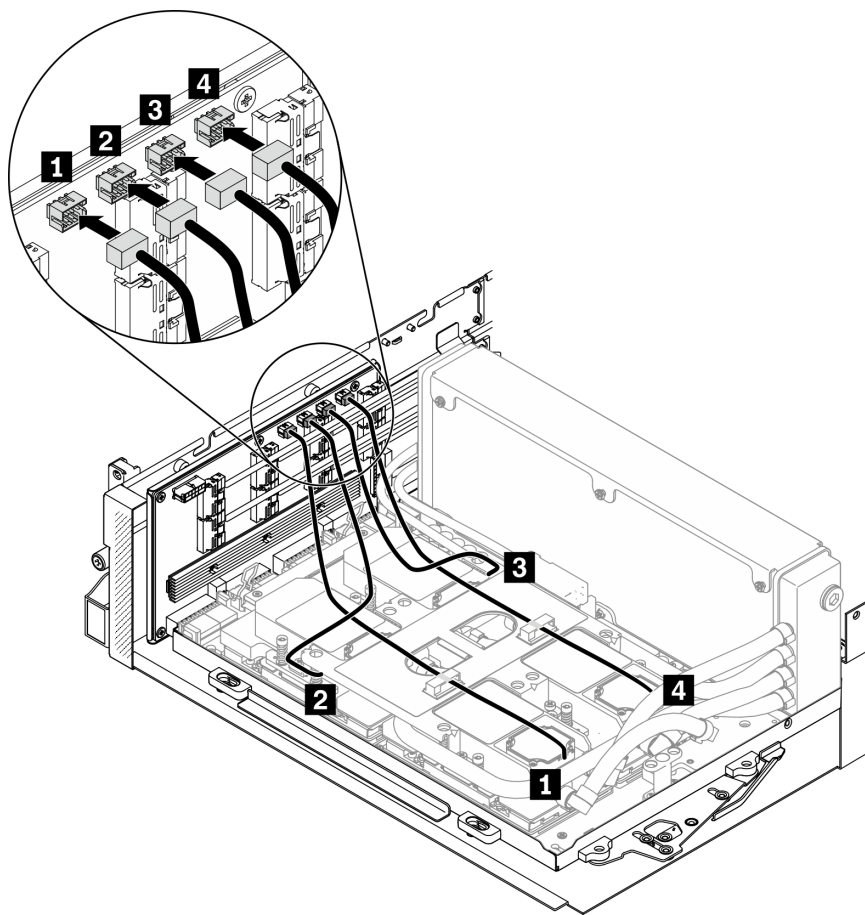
Conexión de los cables de bomba conjunto de placa de frío al conjunto de retemporizador
